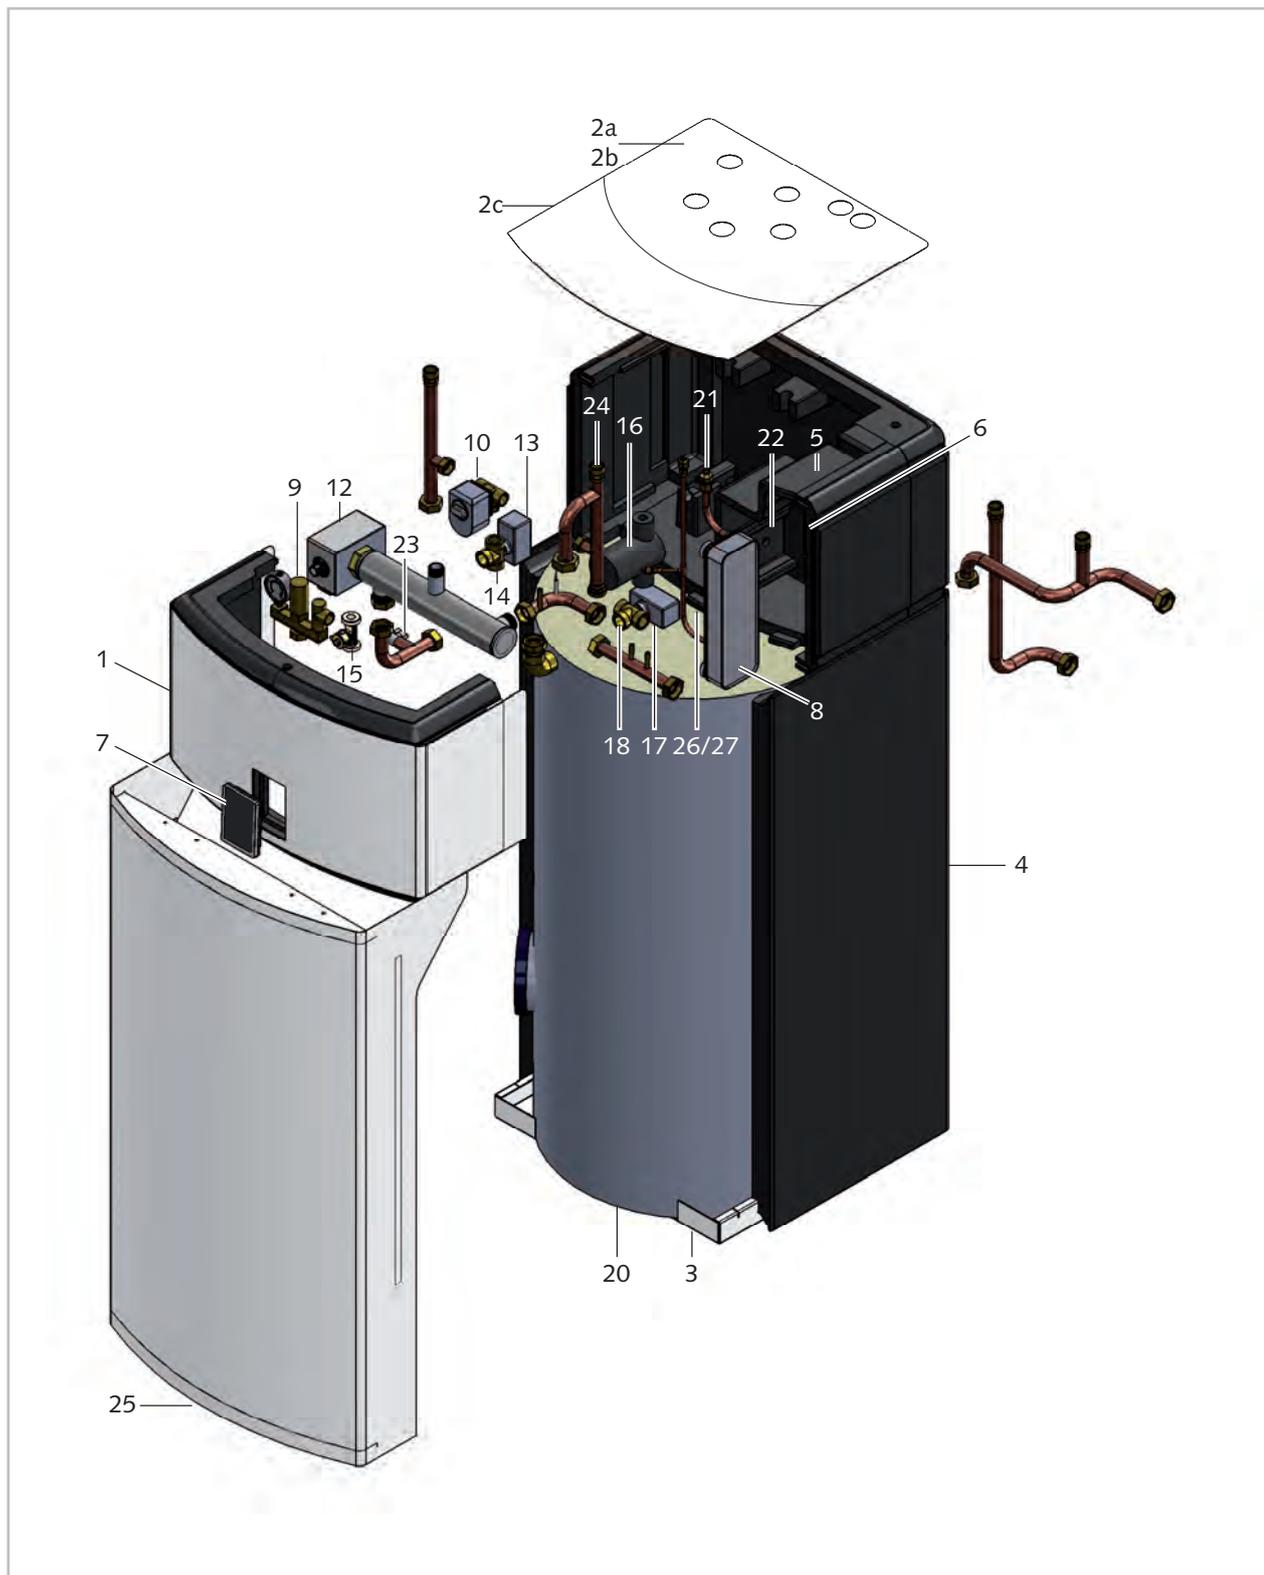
Vue éclatée du module interne WKF-compact 70/120/180
